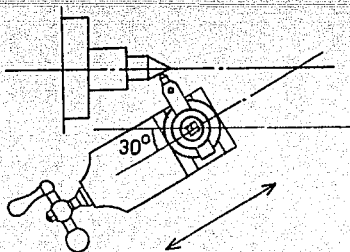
El carro auxiliar ha sido girado 60° desde su posición original hacia el cabezal principal.
